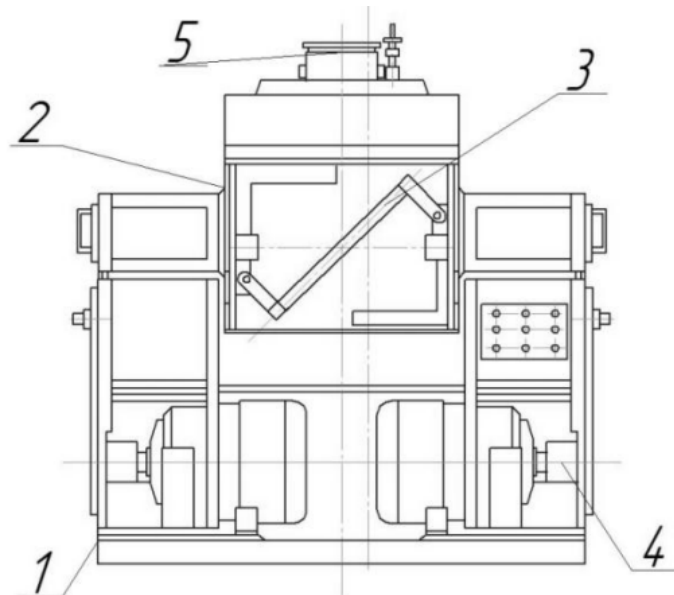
Загальний вигляд тістомісильної машини Ш2-ХТ2-І: 1 - станина; 2 - місильна ємність; 3 - сполучна штанга; 4 - привод; 5 - нерухома кришка
